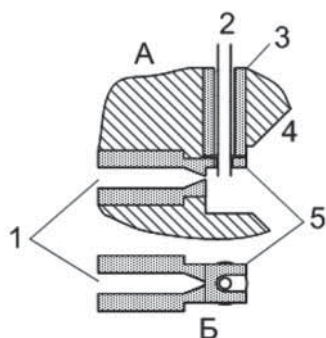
Устройство дополнительной фиксации взаимоположения сопел распылителя HECFMN [20, 231]: А — вид сбоку; Б — вид снизу; 1 — газовая трубка; 2 — жидкостной капилляр; 3 — защитная трубка; 4 — участок корпуса; 5 — U-образная вилка
